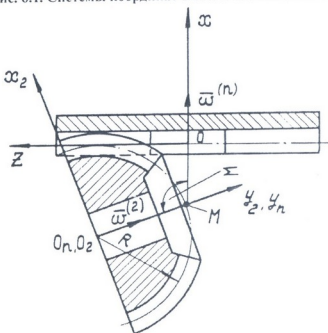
Станочное зацепление при нарезании полусферического зубчатого колеса
